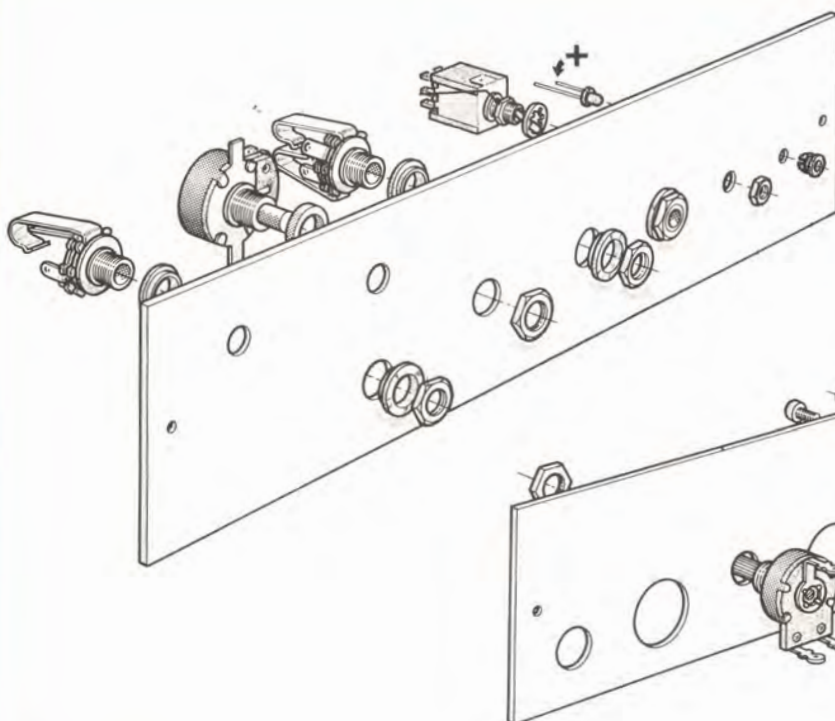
Fissaggio dei comandi sul pannello frontale.
